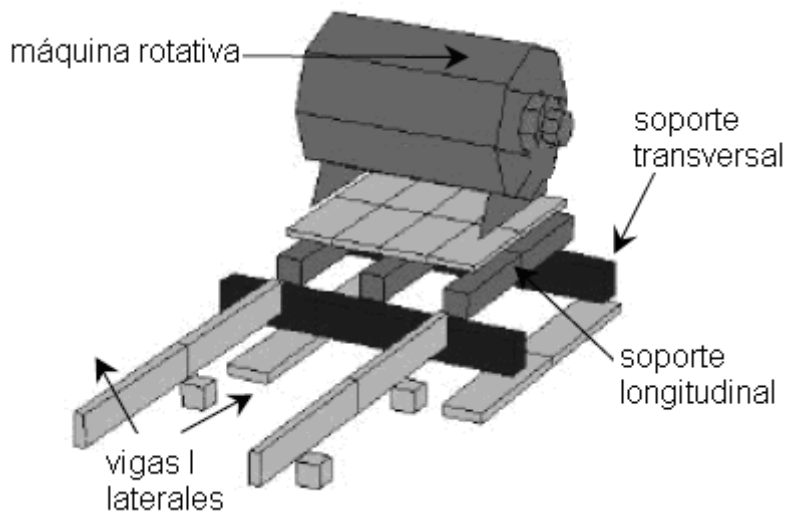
Conjunto de vigas soporte de máquina rotativa.
